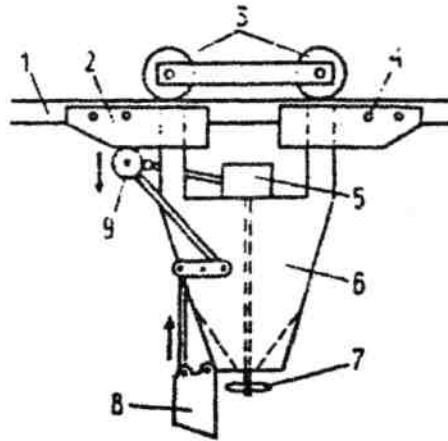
Устройство для раздачи корма в рыбоводных бассейнах: 1 — направляющая; 2 — копиры; 3 — ролики; 4 — зажимы; 5 — редуктор; 6 — бункер; 7 — пропеллерный разбрасыватель; 8 — заслонка; 9 — приводной дополнительный ролик
